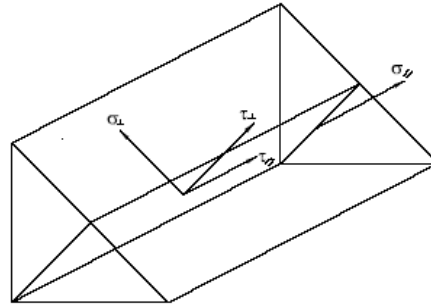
Tensiones en el plano de garganta e un cordón de soldadura
